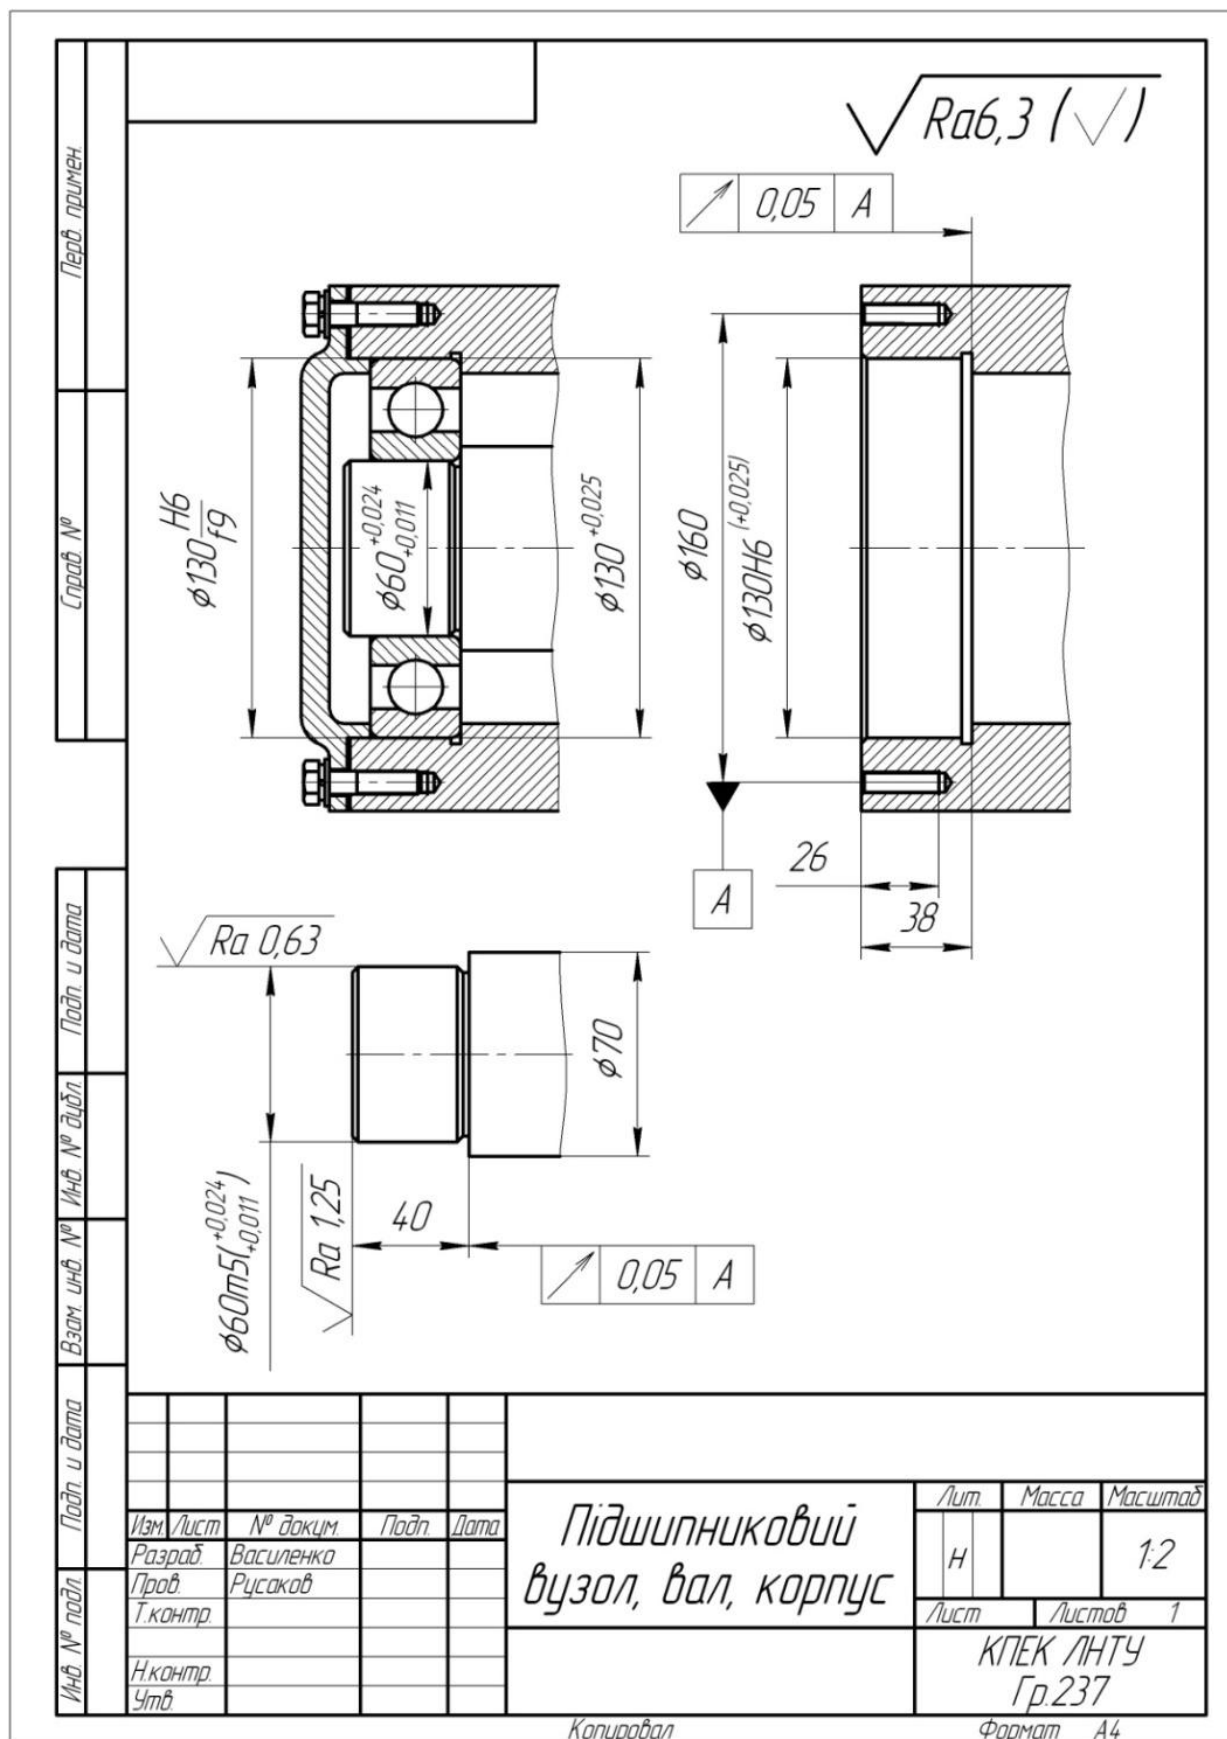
Приклад оформлення креслення з'єднань кілець вальниці котіння з валом та корпусом
